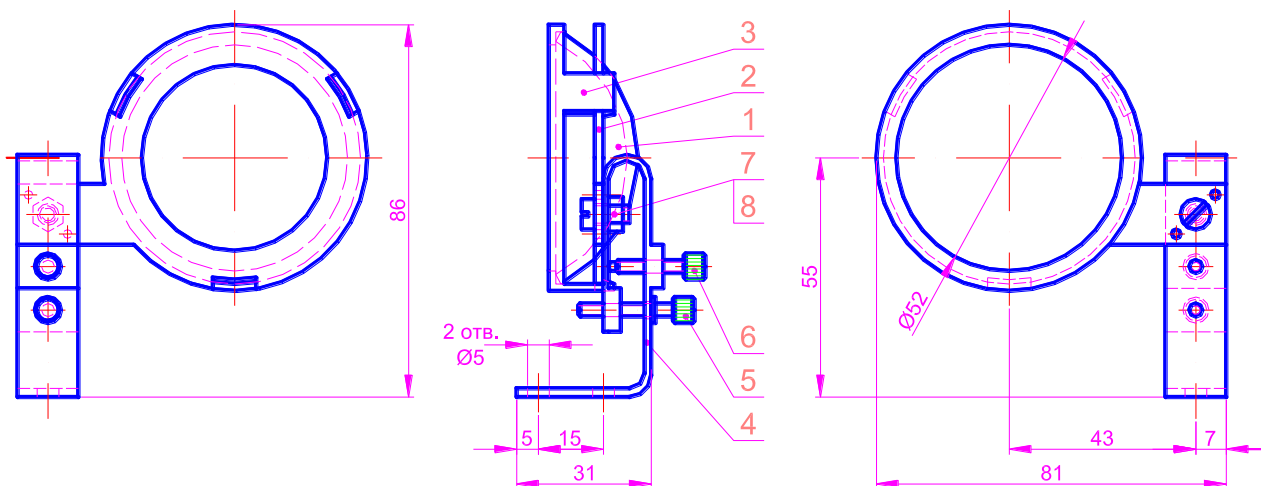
Кресленик спроектованого вузла юстирування: 1 – сферичне дзеркало; 2 – основа; 3 – оправа; 4 – пружний кронштейн; 5 – регулювальний гвинт; 6 – кріпильний гвинт; 7 – гайка; 8 – гвинт
